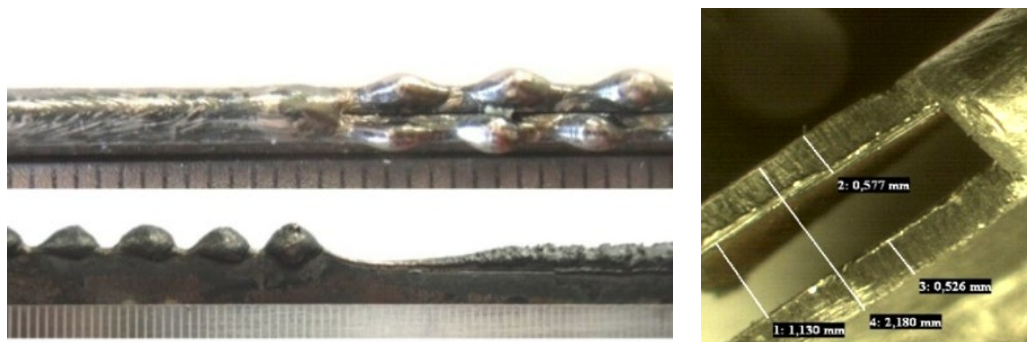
Применение колебаний дуги в МП при сварке торцевых соединений
